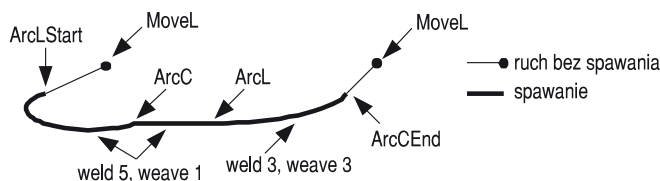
Modyfikacje ścieżki spawania w dodatku ArcWelding PowerPac
